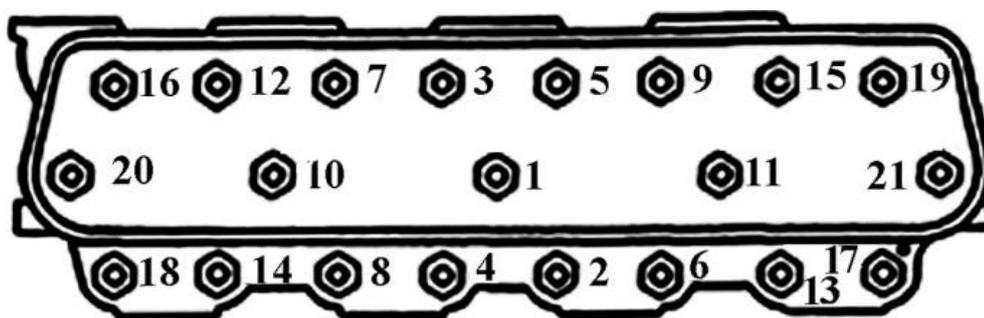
Порядок затяжки гаек крепления головки цилиндров
